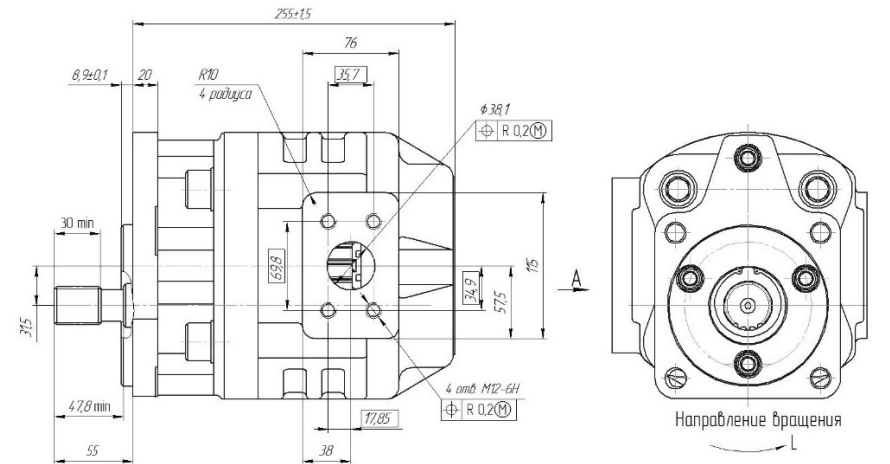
Габаритные и присоединительные размеры GP4BF100R-B736W 21.
